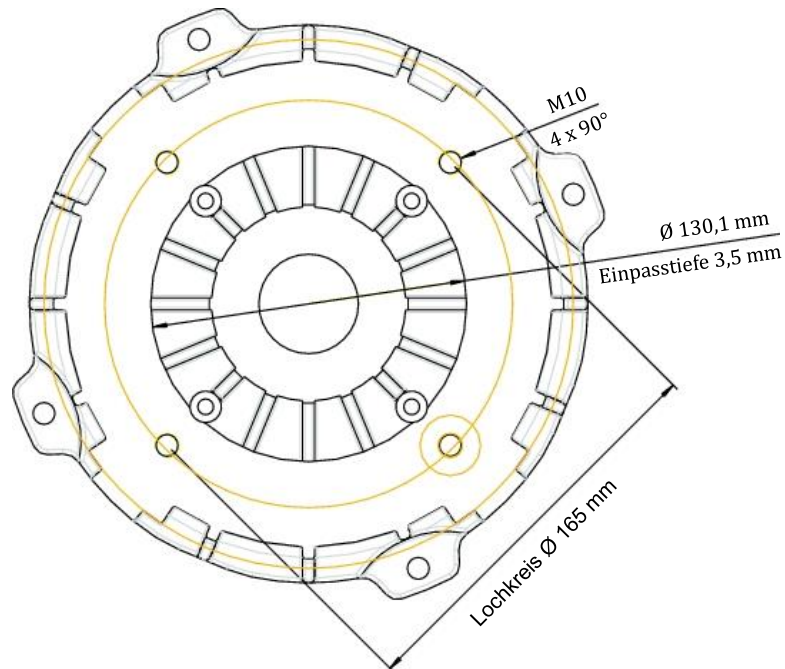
Flansch für Hydraulik- und Getriebeantriebe
